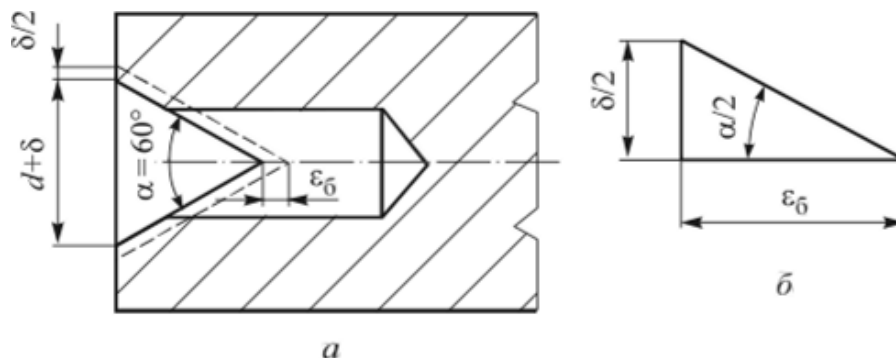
Схема виникнення похибки базування під час встановлення заготовки на «жорсткий» центр
